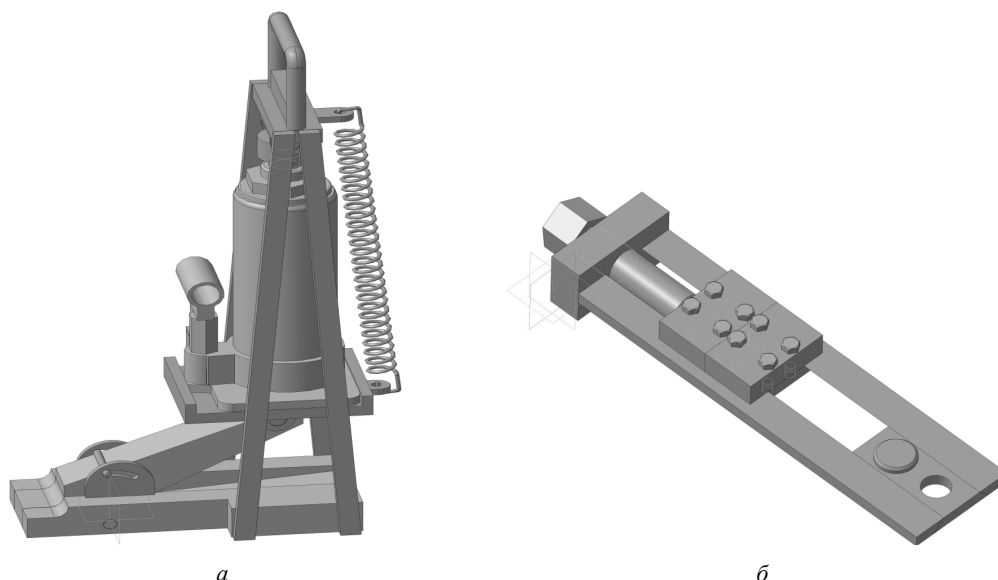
Приспособления для перемещения машин преобразовательного агрегата:
